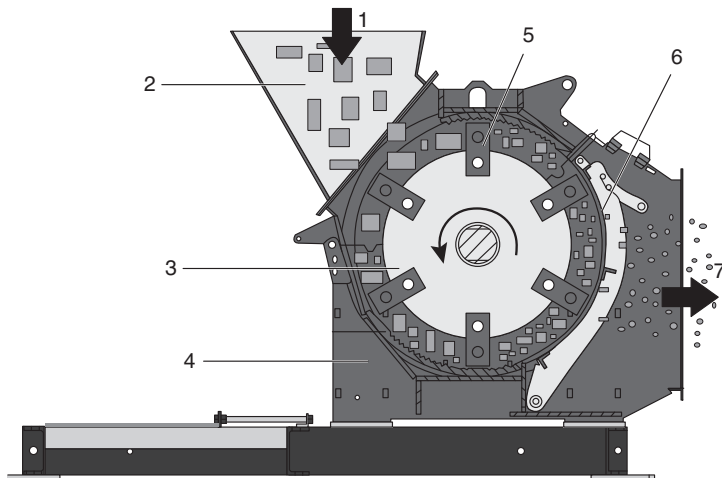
Молотковая мельница: 1 — измельчаемый материал корпус; 2 — загрузочный бункер; 3 — ротор; 4 — корпус; 5 — молоток; 6 — колосниковая решетка; 7 — измельченный материал
